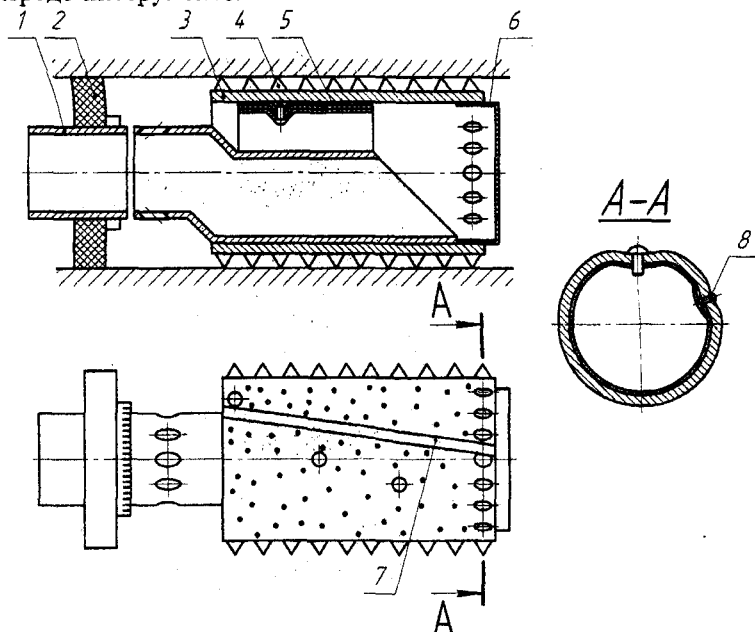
Схема катода с гибкой металлической обечайкой
